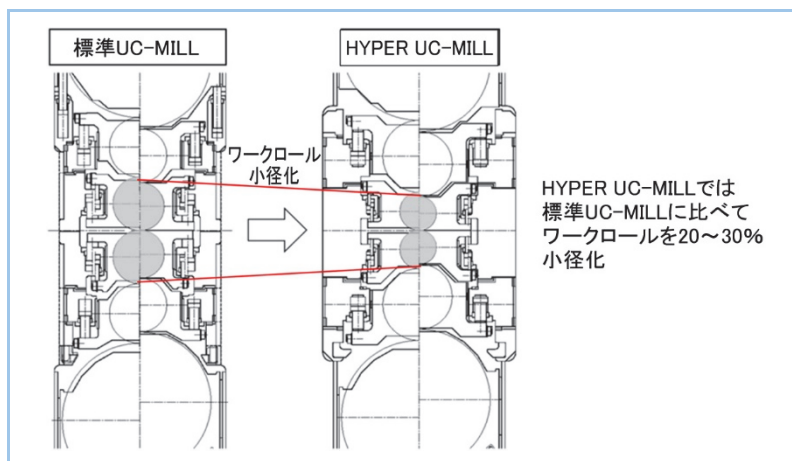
標準 UC-MILL 及び HYPER UC-MILL のロール配置
